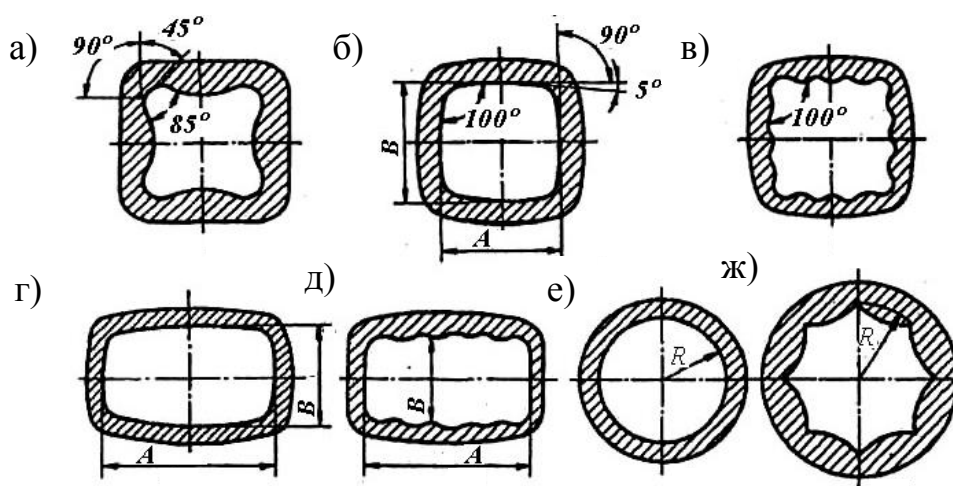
Виды поперечного сечения изложниц для отливки стальных слитков:
